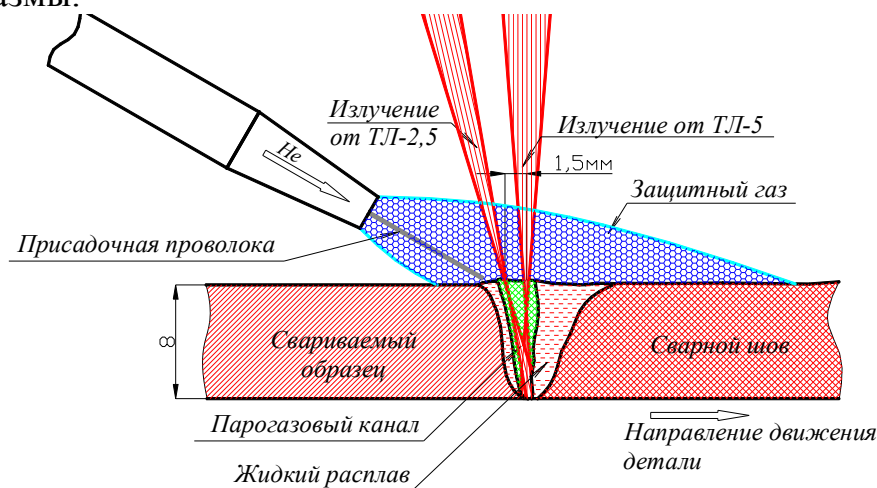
Оптимальная схема двухлучевой лазерной сварки.
